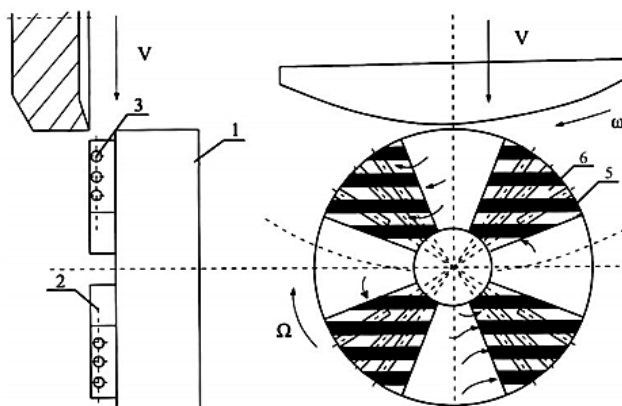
Схема осьового підшипника, виготовленого з використанням комплексної термофрикційної та механічної обробки
